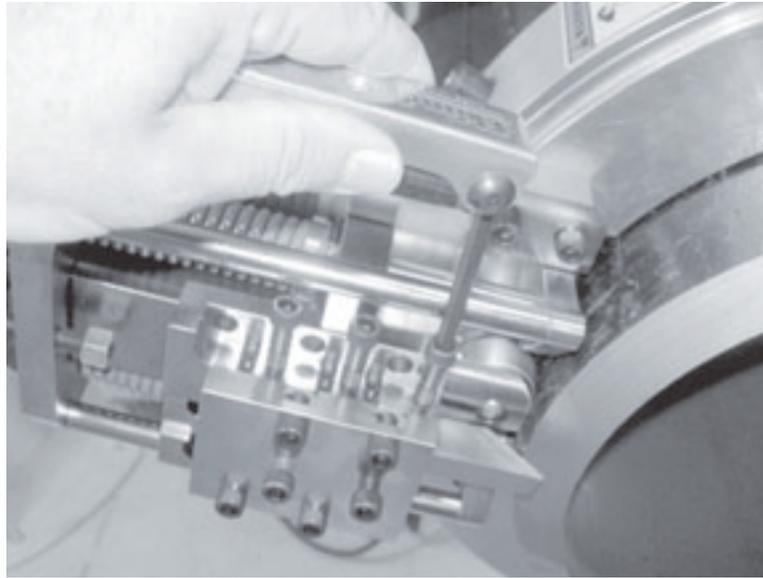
Führen Sie das Anfaswerkzeug wie dargestellt in den Werkzeughalter ein.
